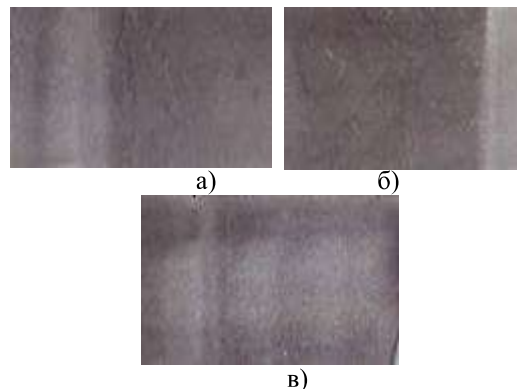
Исследуемый образец внутренней поверхности гильзы цилиндра с характерными признаками износа: а) – наплывы металла поршня; б) – следы схватывания металла; в) – натирсы и образовавшиеся белые слои
